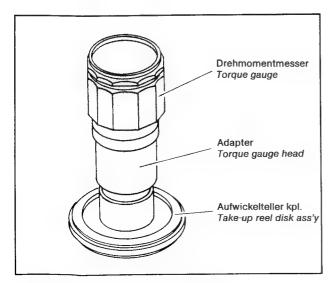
Drehmomentmesser aufsetzen Fig. 2-24 Take-up torque
